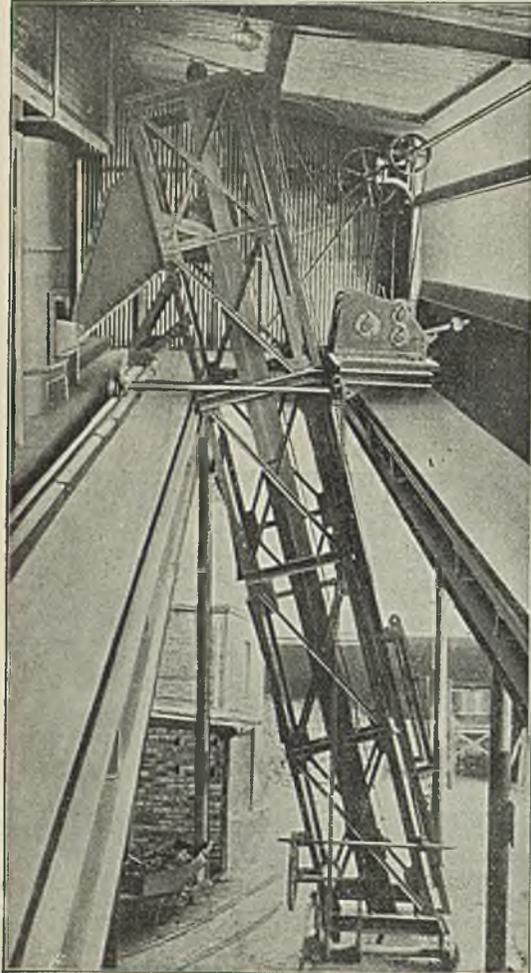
Fahrbarer Kupolofenschrägaufzug.
